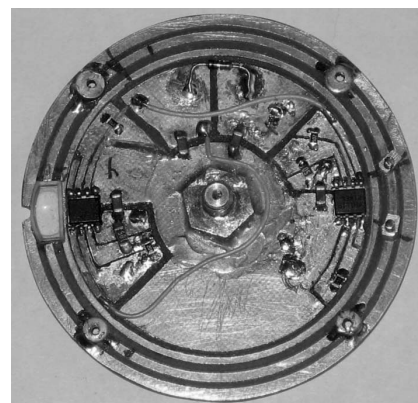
Внешний вид сенсорной головки (вид с обратной стороны)
